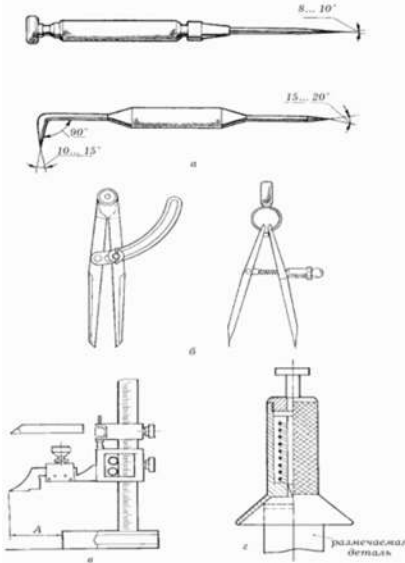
Разметочные инструменты: а – чертилки; б – циркули; в – штангенрейсмус; г – кернер-центроискатель
